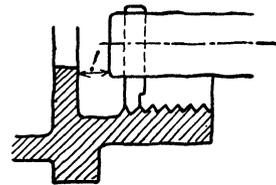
c. Innengewinde, richtig (Vgl. DIN 2352).
